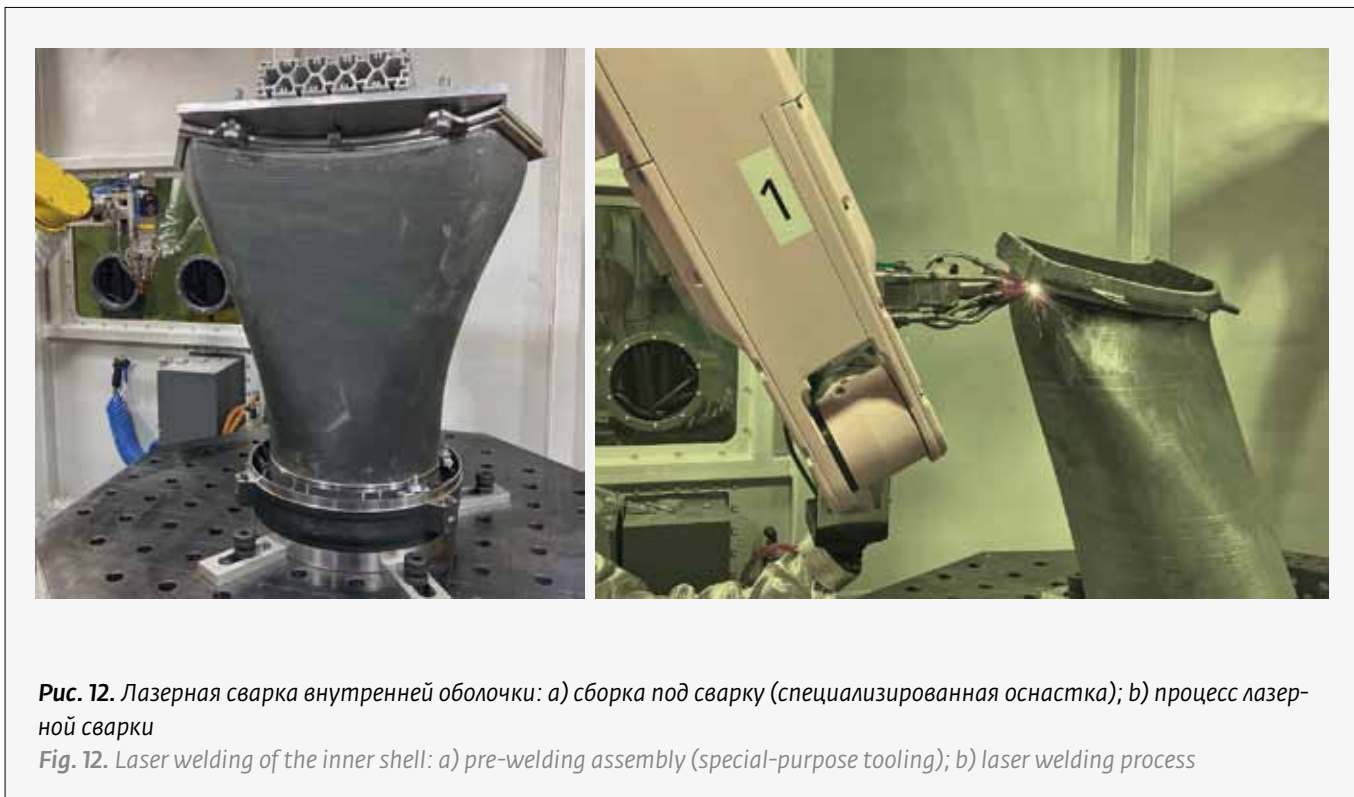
Лазерная сварка внутренней оболочки: а) сборка под сварку (специализированная оснастка); б) процесс лазерной сварки
